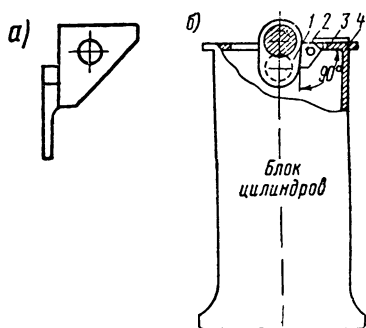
Приспособление (угольник) для проверки внутренней мертвой точки верхнего поршня и его установка на блоке:
